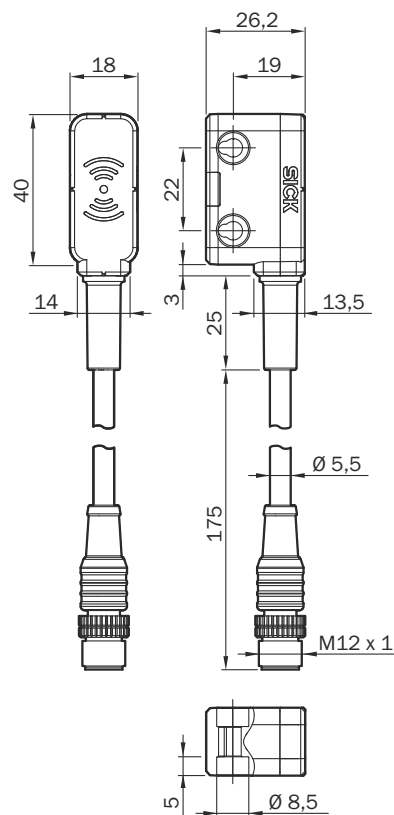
Maßzeichnung STR1 Sensor mit M12-Stecker
